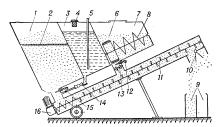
Смеситель отравленных приманок: 1— зерновой бункер; 2— сетка; 3— резервуар для масла; 4— заливная горловина с фильтром; 5— уравнительная трубка; 6— щётки для очистки выходного отверстия бункера пестицидов; 7— бункер пестицидов; 8— проволочный шнек; 9— тара; 10— перекидная заслонка выгрузного отверстия смесителя; 11— шнек-смеситель; 12— заслонка выходного отверстия бункера пестицидов; 13— дозирующие барабанчики; 14— регулировочный кран; 15— заслонка зернового бункера; 16— электродвитатель. двигатель.
